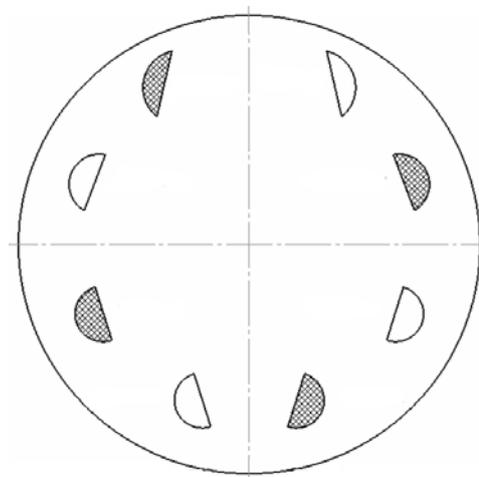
Схема закрепления карбидокремниевых пластин на планшайбе (заштрихованы шлифованные с одной стороны пластины, без штриховки показаны необработанные заготовки)
